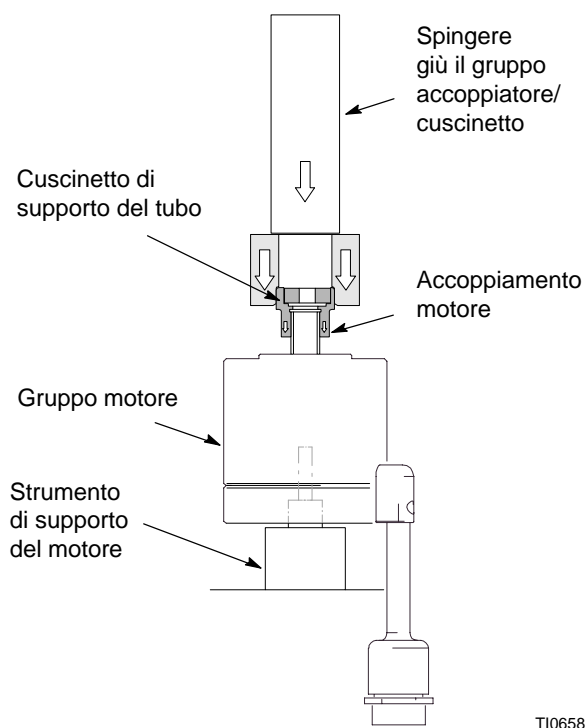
Montaggio del cuscinetto di supporto del tubo
